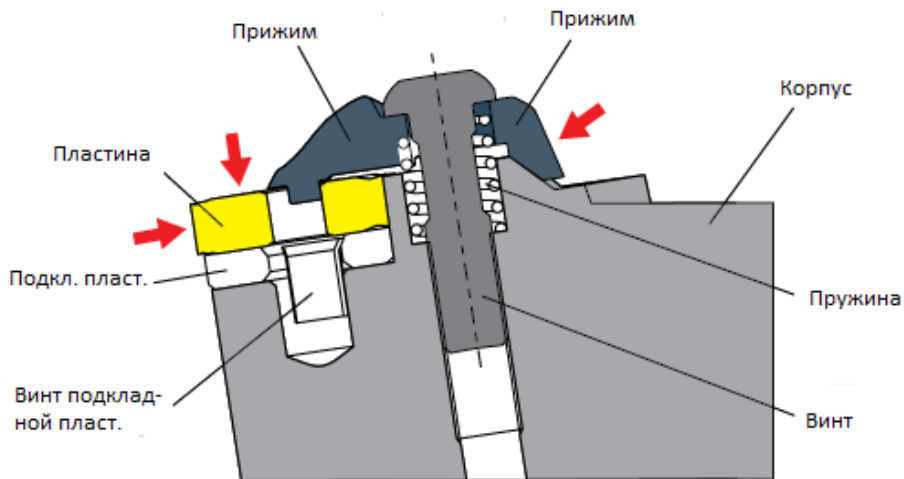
Державка для резца DCLNR/L-2020K12.
